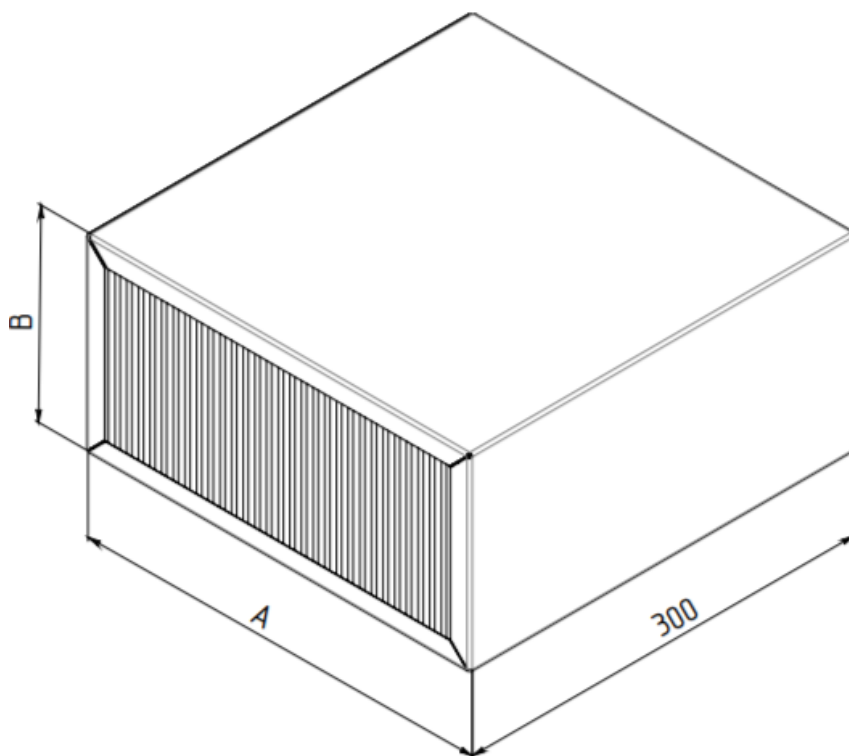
Внешний вид и основные размеры фильтрующих вставок SPH
